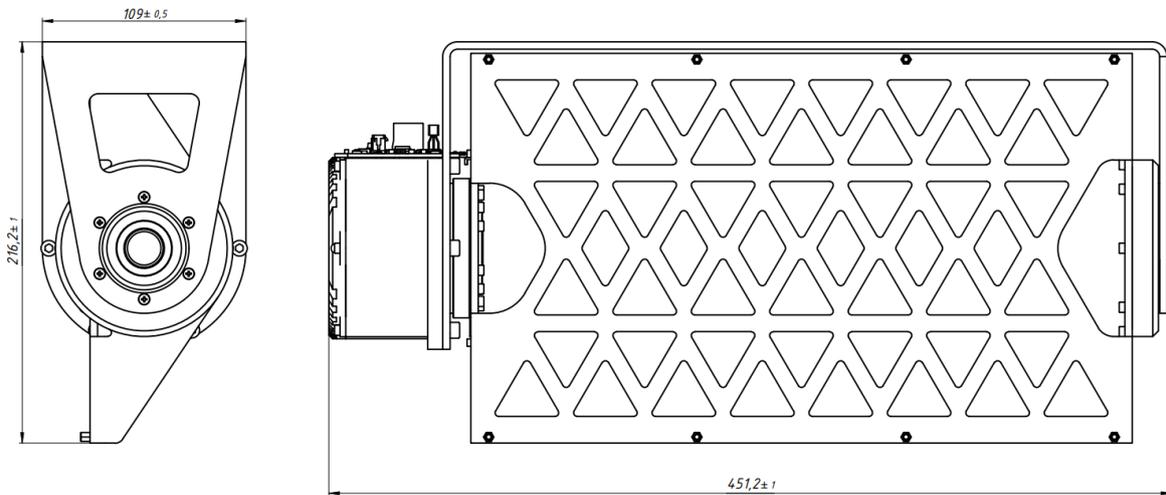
Габаритные размеры бортового наклонного устройства
